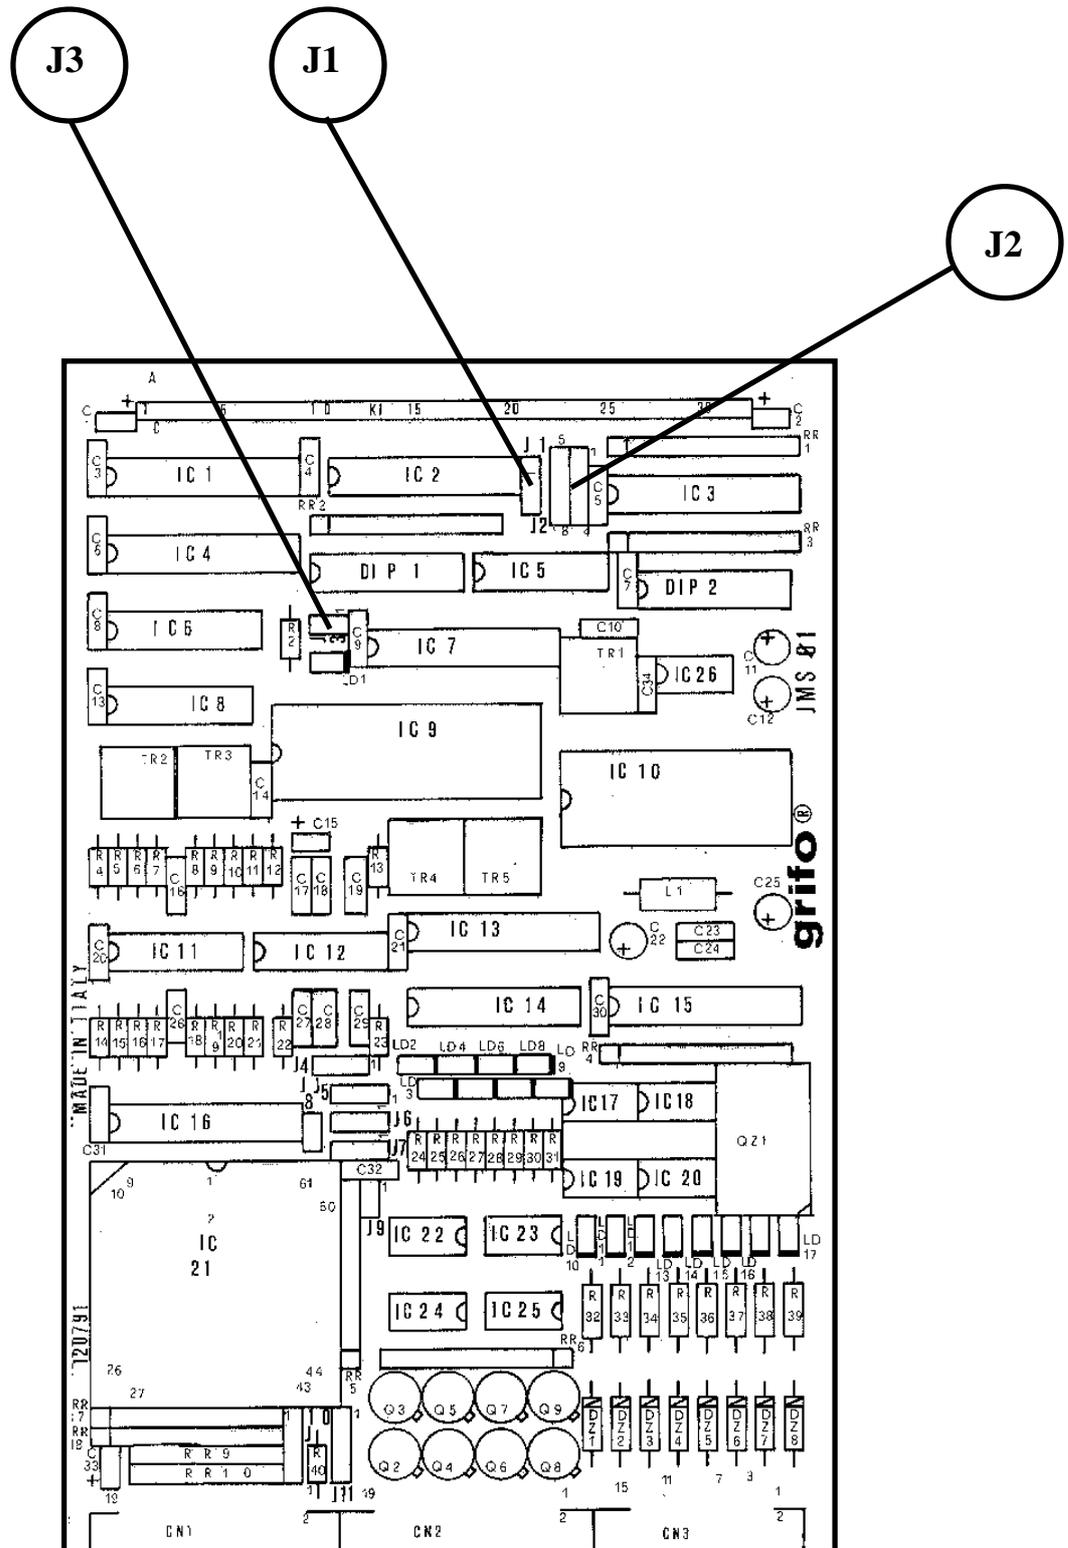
DISPOSIZIONE JUMPERS SEZIONE INTRAFACCIMENTO
